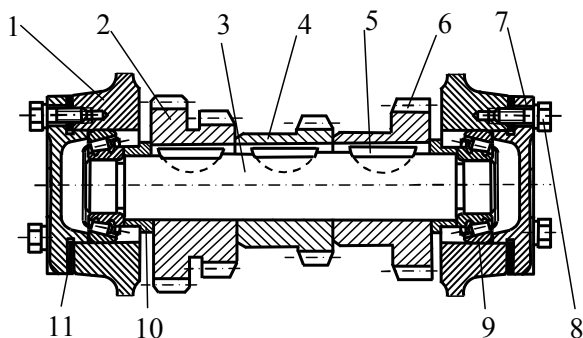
Промежуточный вал с неподвижными шестернями:
